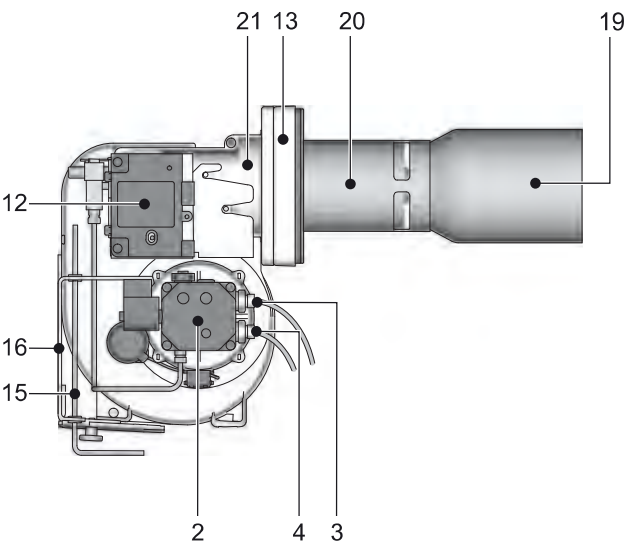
Brûleur à fioul - vue latérale de gauche
